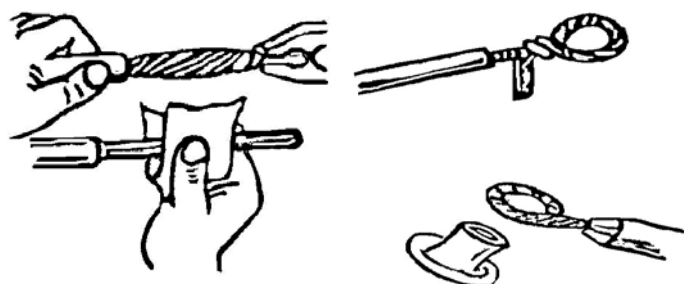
Подготовка жилы и наконечника для опрессовки
